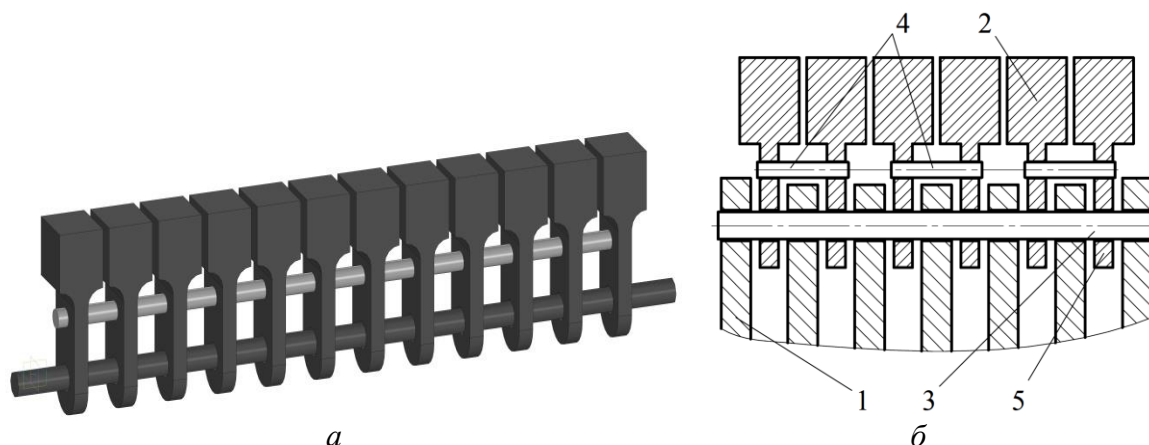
Усовершенствованная конструкция ротора молотковой дробилки: *а* – общий вид навески с комбинированным креплением всех молотков на оси ротора; *б* – схема навески с комбинированным креплением пар молотков
